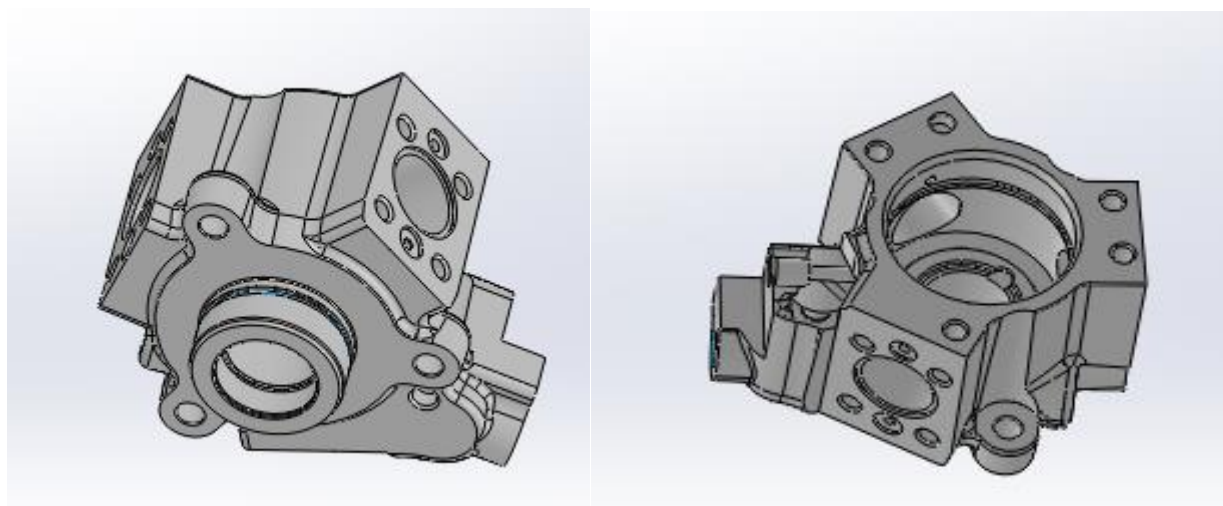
3D model upínacího přípravku pro plastovou komponentu - Carfit
